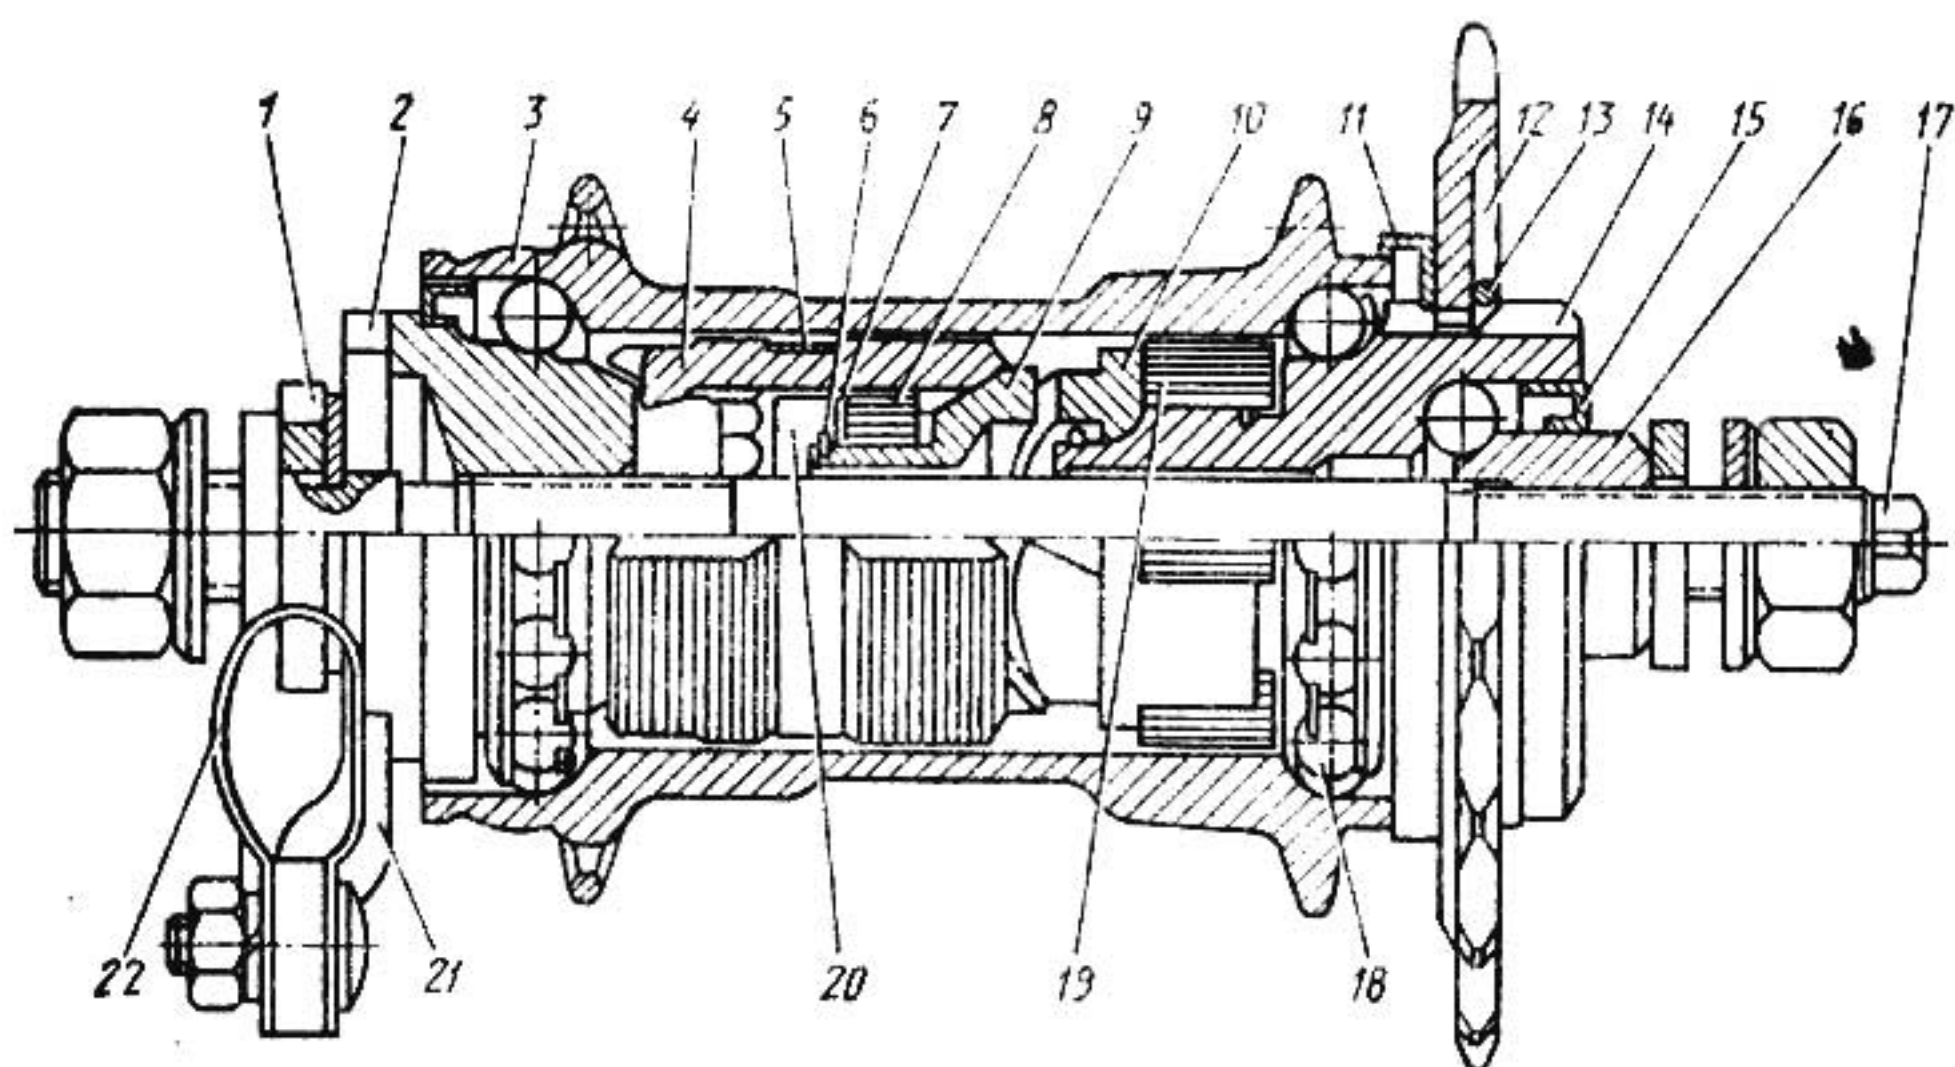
Конструкция втулки заднего колеса типа «Торпедо»:
